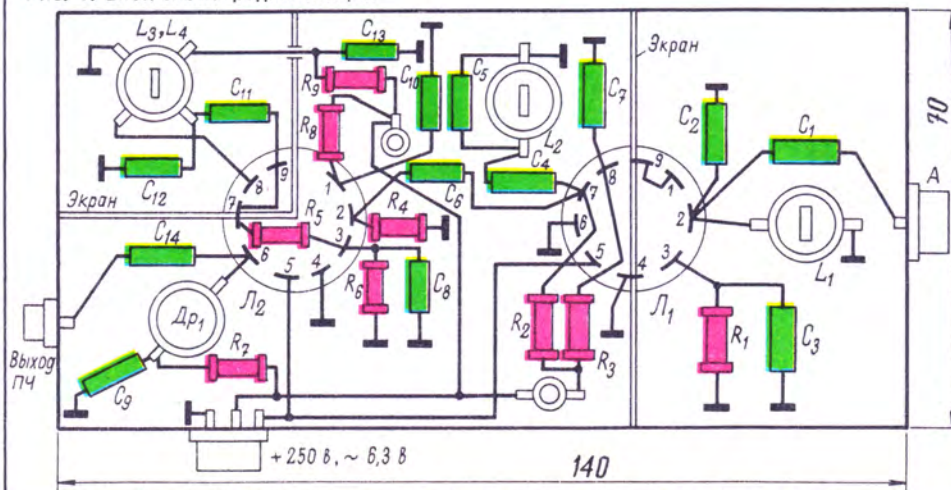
Расположение деталей на шасси конвертера (вид снизу)
